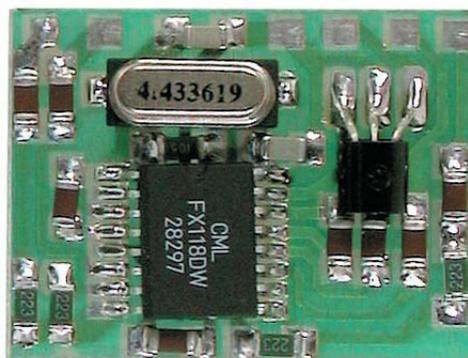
Un des prototypes avant soudure des pattes au pas de 2,54 mm (en haut).
